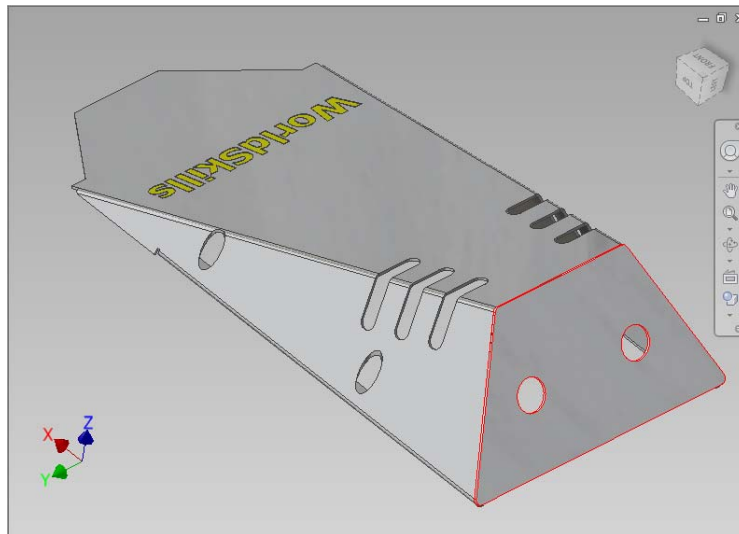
Submontaje de la soldadura de la cubierta superior
